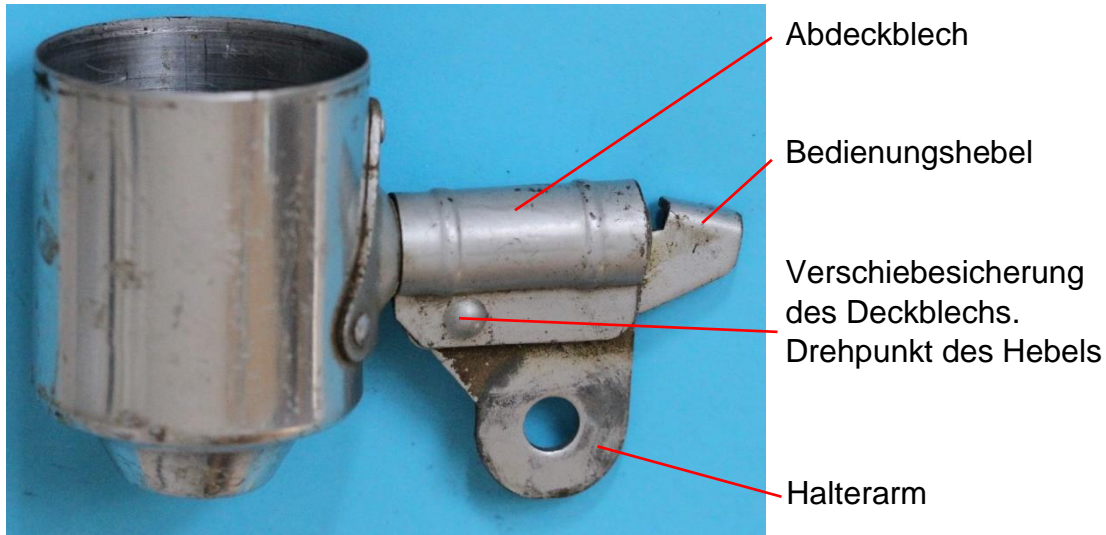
Kippvorrichtung mit einem Dreieckflansch am Mantel befestigt
